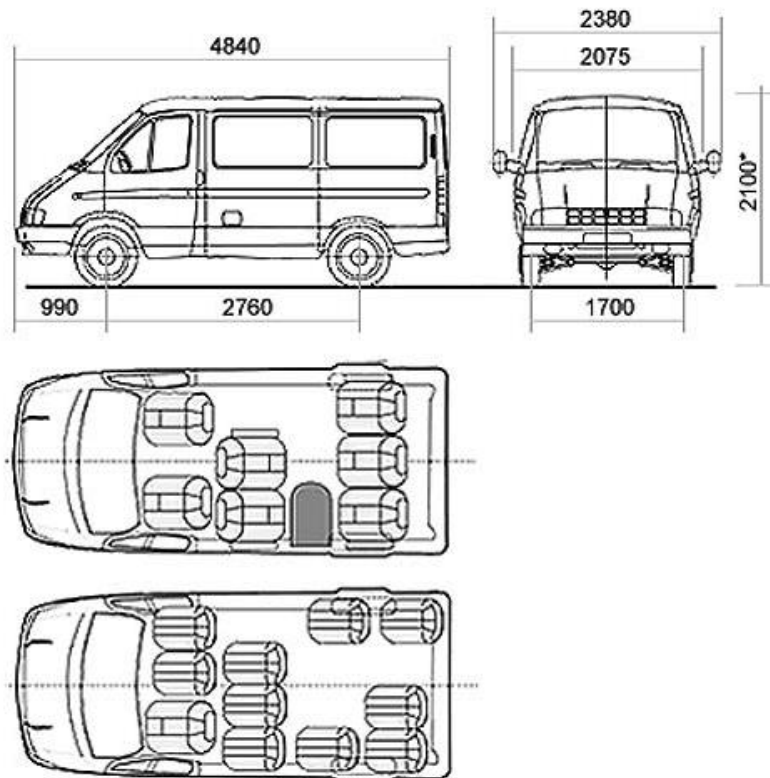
Габаритні розміри автомобіля ГАЗ-33023
